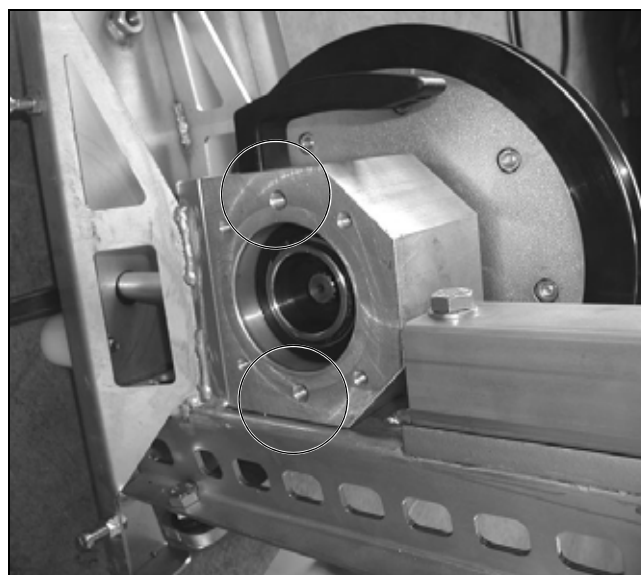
Смонтированный (передний) пакет роликов (блок) с приводным колесом (со стороны фланца крепления мотора)
